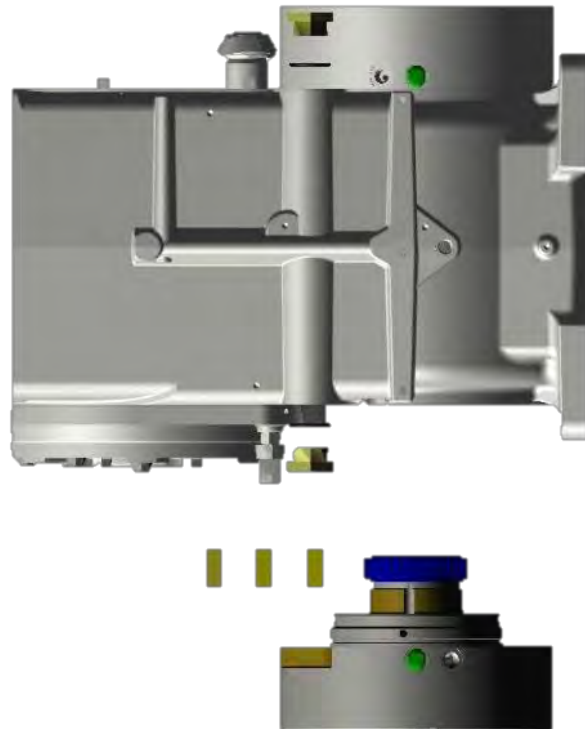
b: "Explosionado del proceso de montaje de la estación 2"
